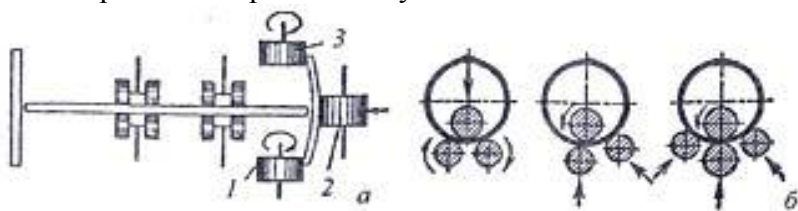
Схемы механической правки сварных двутавровых балок (*а*) и цилиндрических оболочек (*б*)
